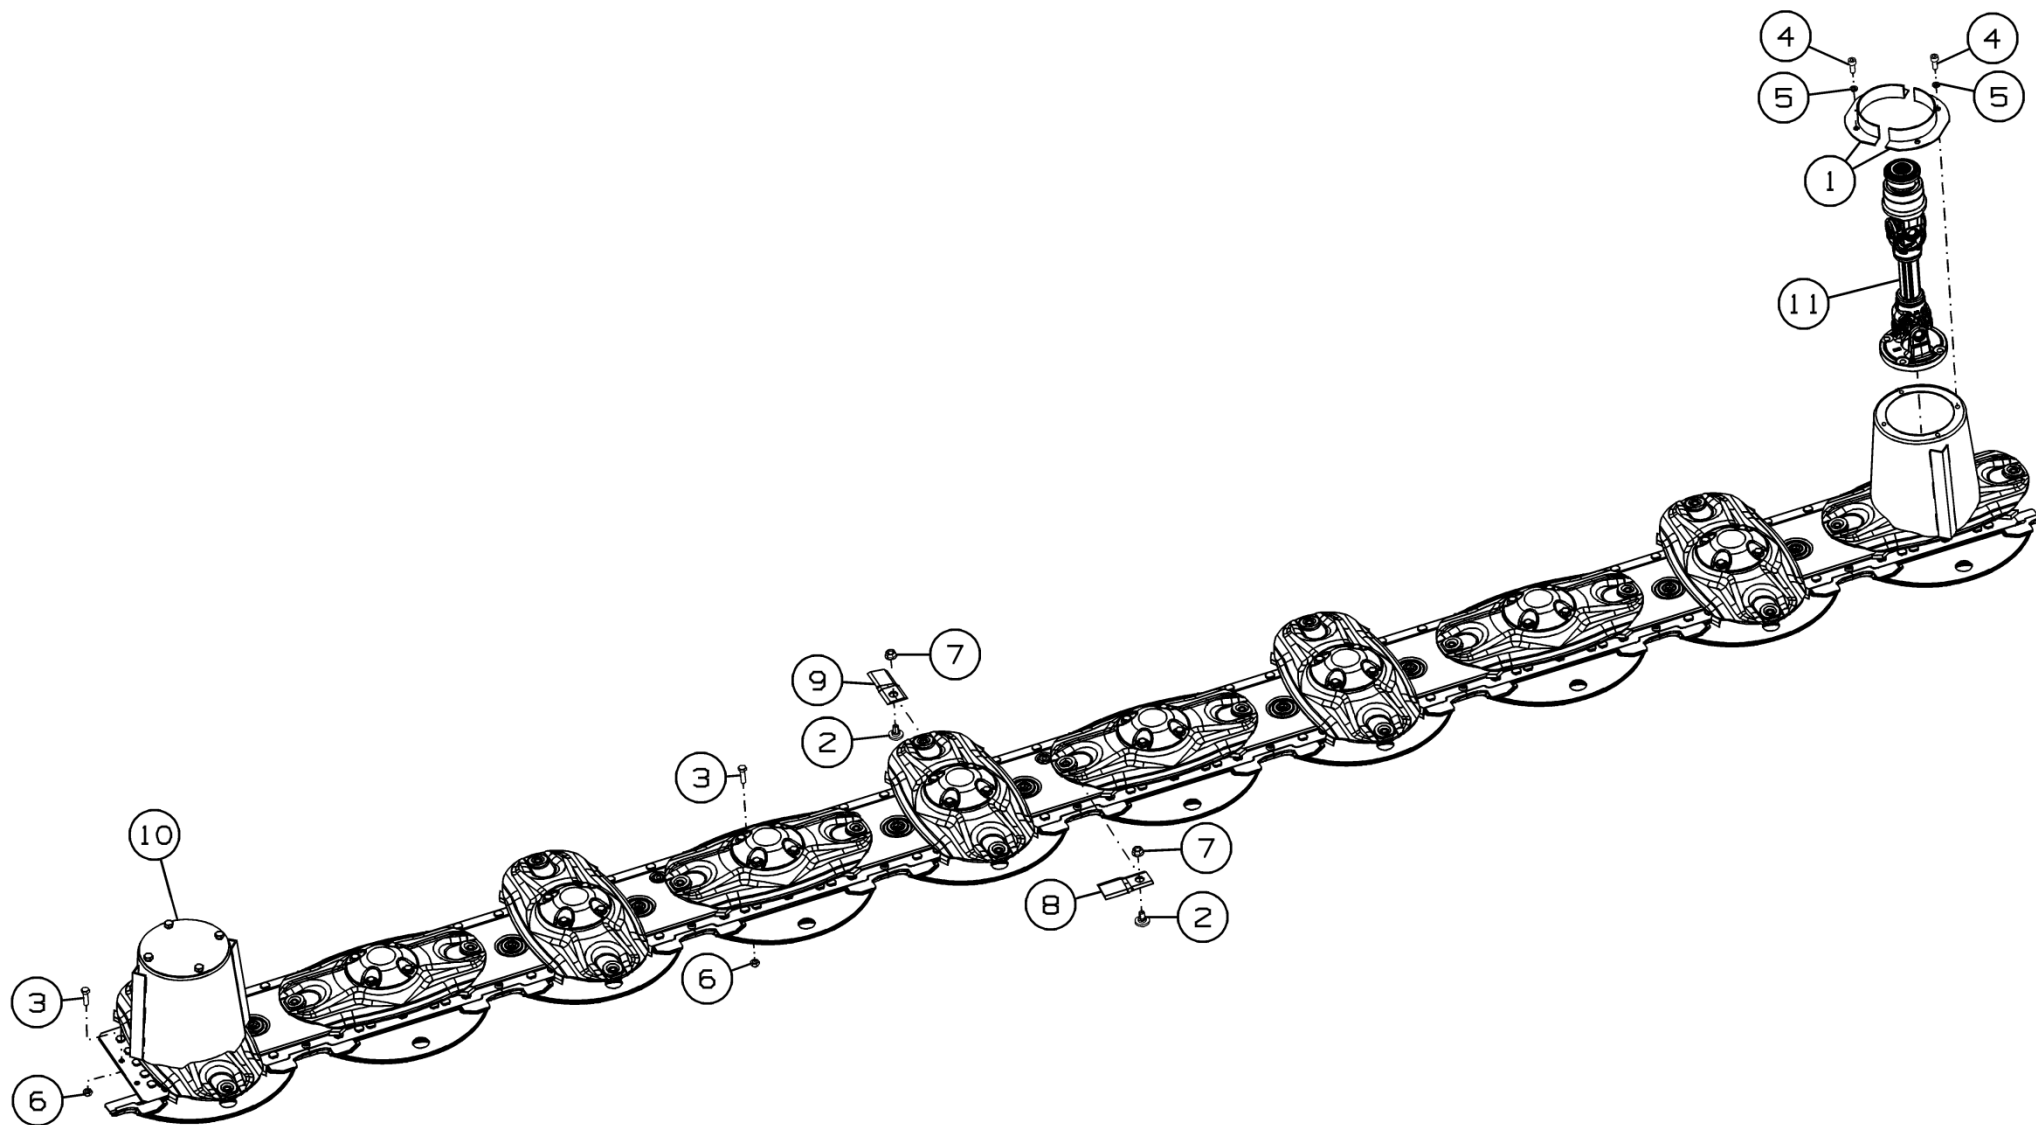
Установка режущего бруса и карданного вала GM-500R.01.04.010
